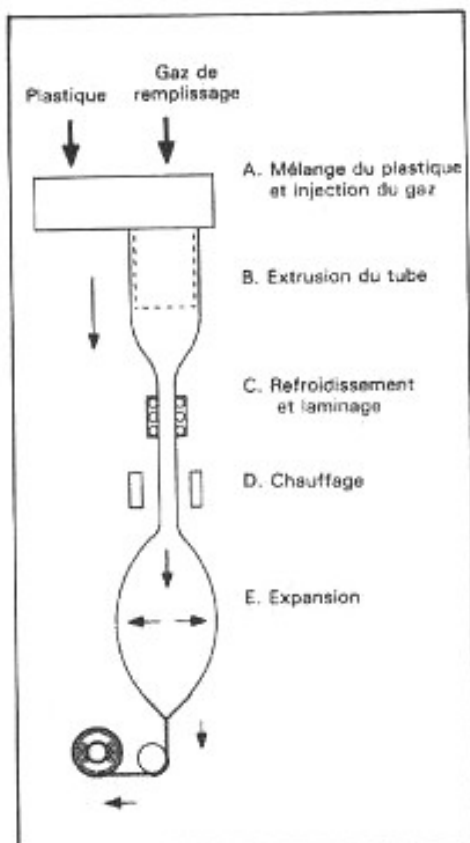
Fabrication du film ETMF (d'après [II]).
